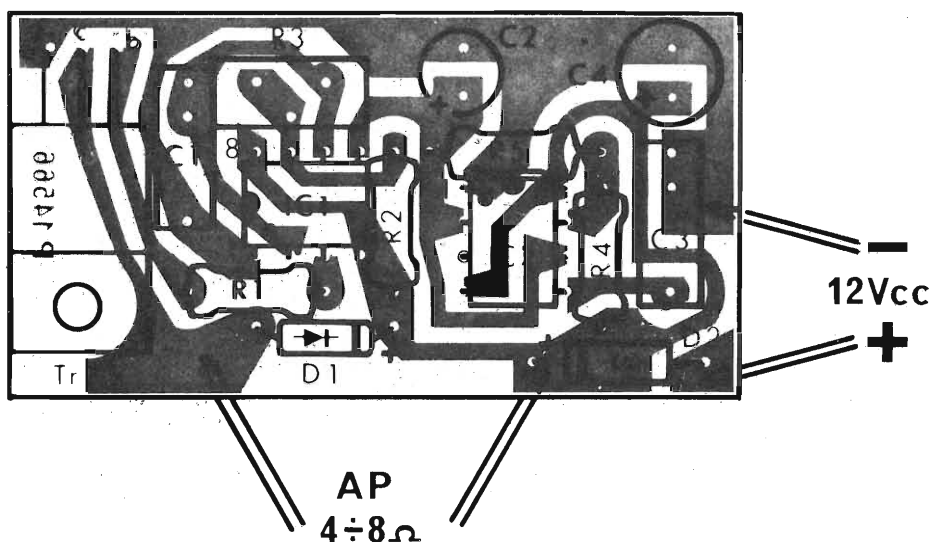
Basetta a circuito stampato vista in trasparenza e disposizione dei componenti.
